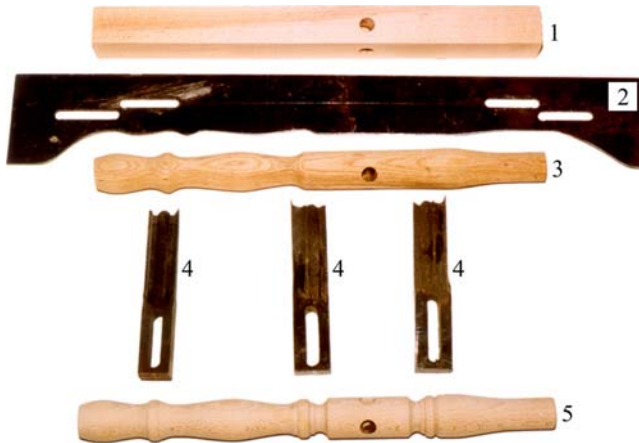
Послідовність технологічного процесу точіння ніжки стільця: 1) заготовка; 2) копер; 3) вигляд заготовки після точіння прохідним різцем під копер; 4) фасонні різці; 5) вид готової деталі ніжки стільця
